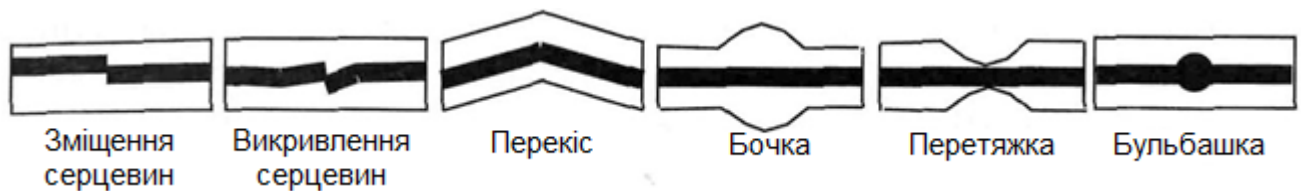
Типи дефектів зварених з'єднань ОВ на дисплеї зварювального апарату
